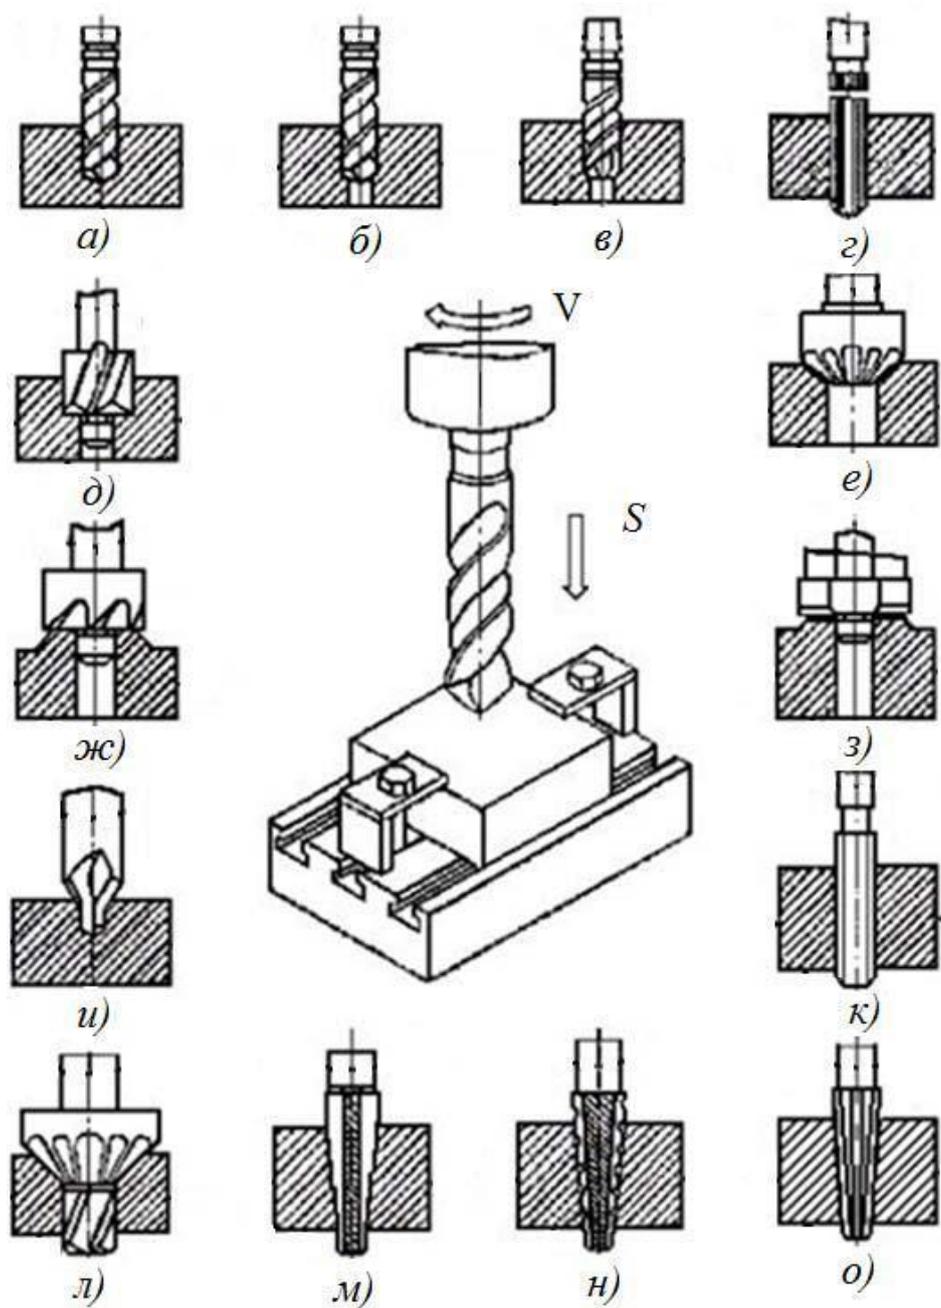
Схема обработки поверхностей на сверлильных станках
